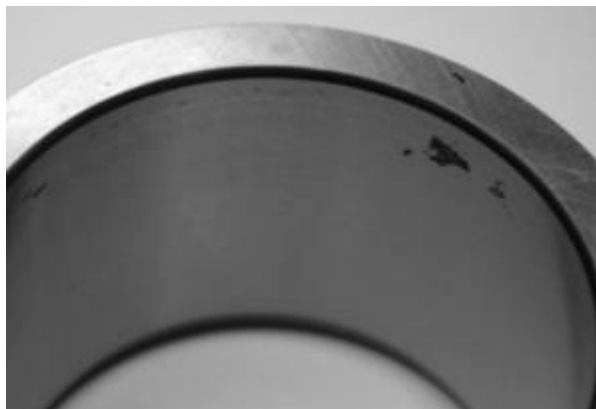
Кільце підшипника кочення з видимими дефектами
